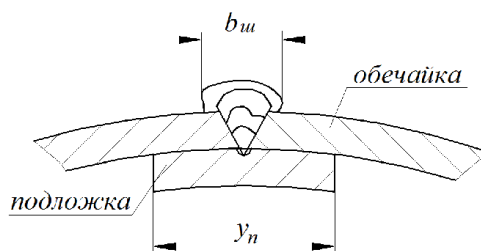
Схема формирования сварного шва обечайки
